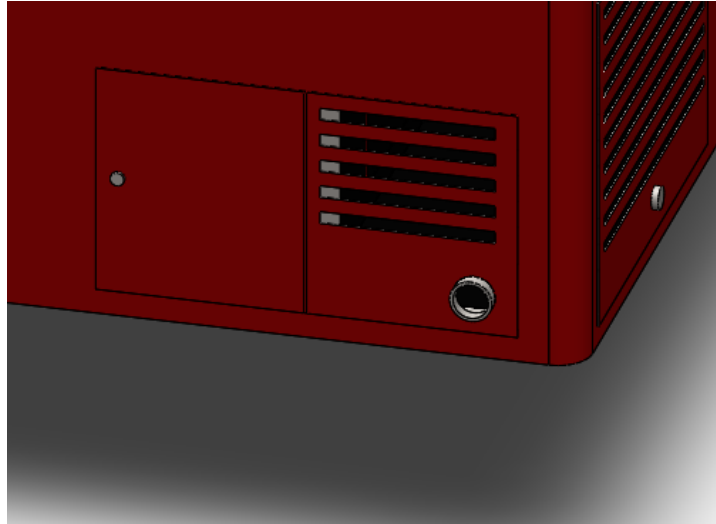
Salida de escape del grupo y habitáculo para elementos de puesta a tierra. Fuente propia
